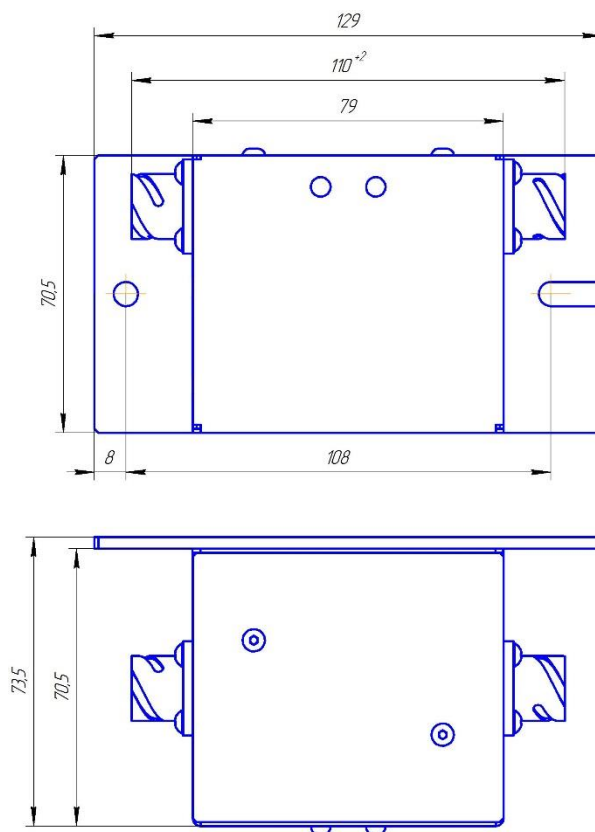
Вид ZET 7156 с монтажной пластиной при установке на вертикальную поверхность
